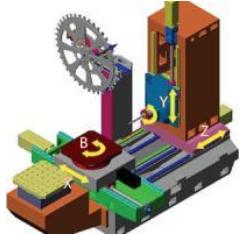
Схема устройства смены инструмента путем относительного перемещения шпинделя: станок горизонтальный сверлильно-фрезерно-расточной с ЧПУ модели 630Н ОАО «Стерлитамакский станкозавод»
